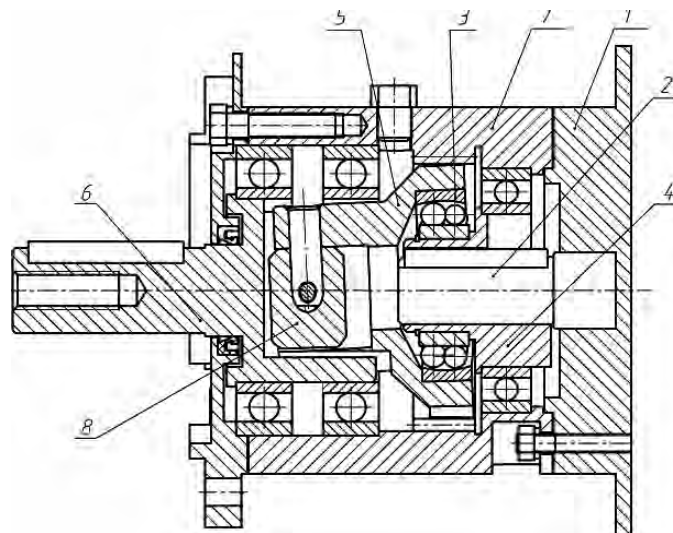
Общий вид мотор-редуктора на базе ППП типа К-Н-V
